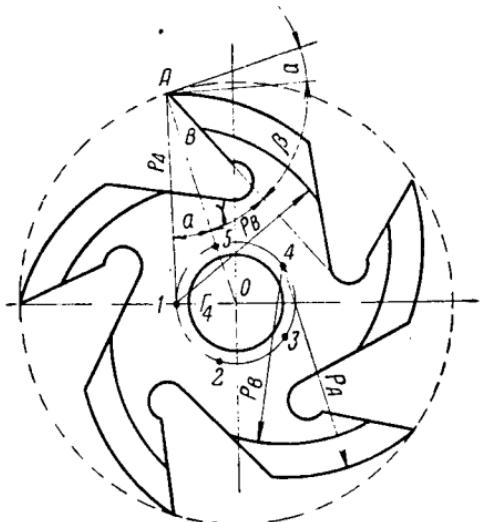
Способ построения затылка зуба фрезы по дуге окружности, центр которой смещен относительно центра фрезы
